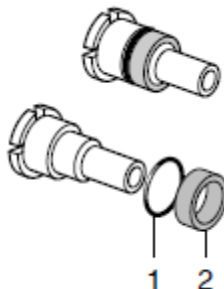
Штуцер с уплотнительным кольцом и пластиковым кольцом
